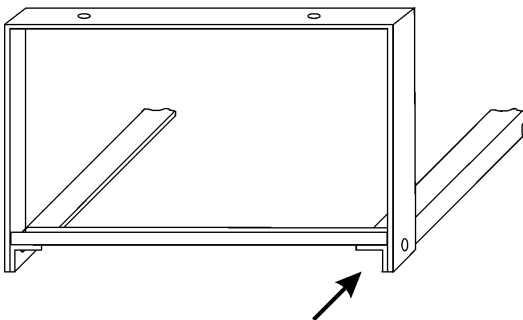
Befestigung eines Wandhalters an der Konsole bei Montageart B), Ansicht von oben
